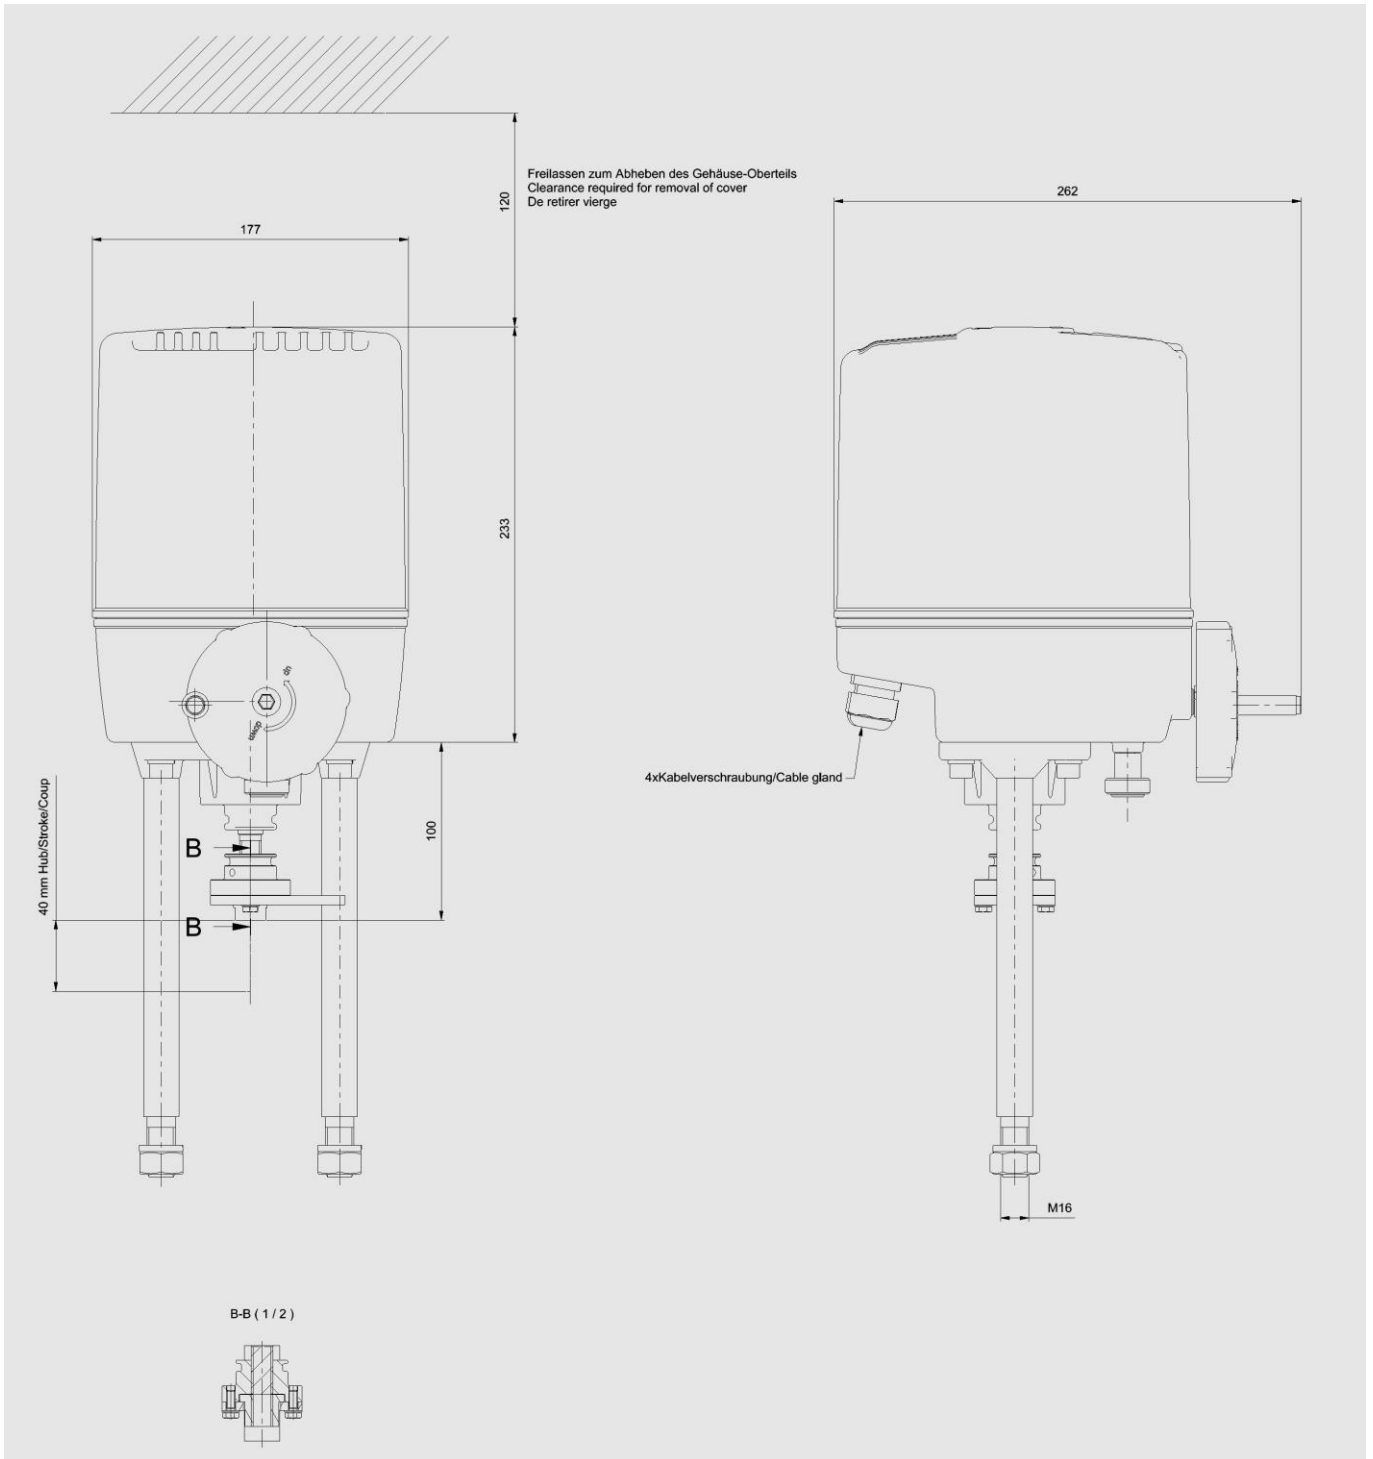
Maßblatt/Dimension sheet/wymiary
